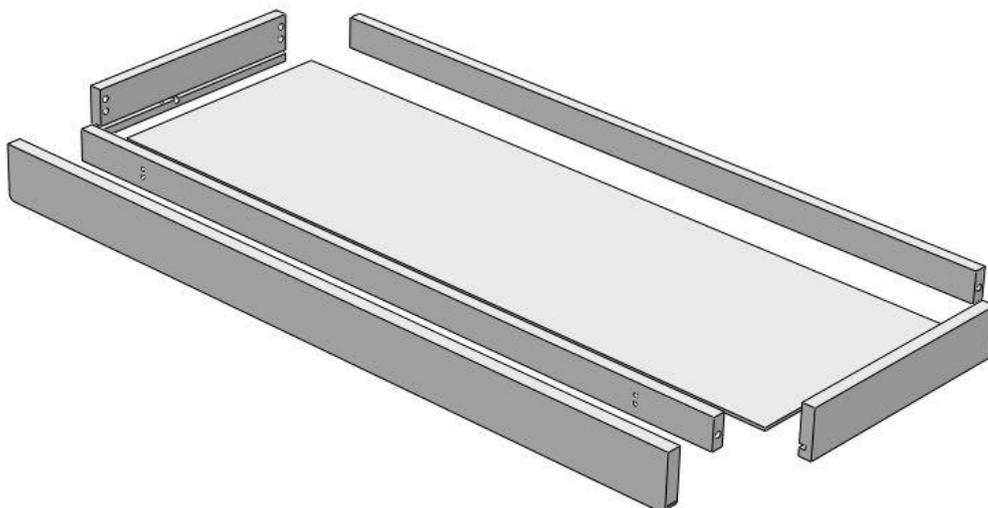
Gaveta inferior em vista isométrica com vista explodida.
